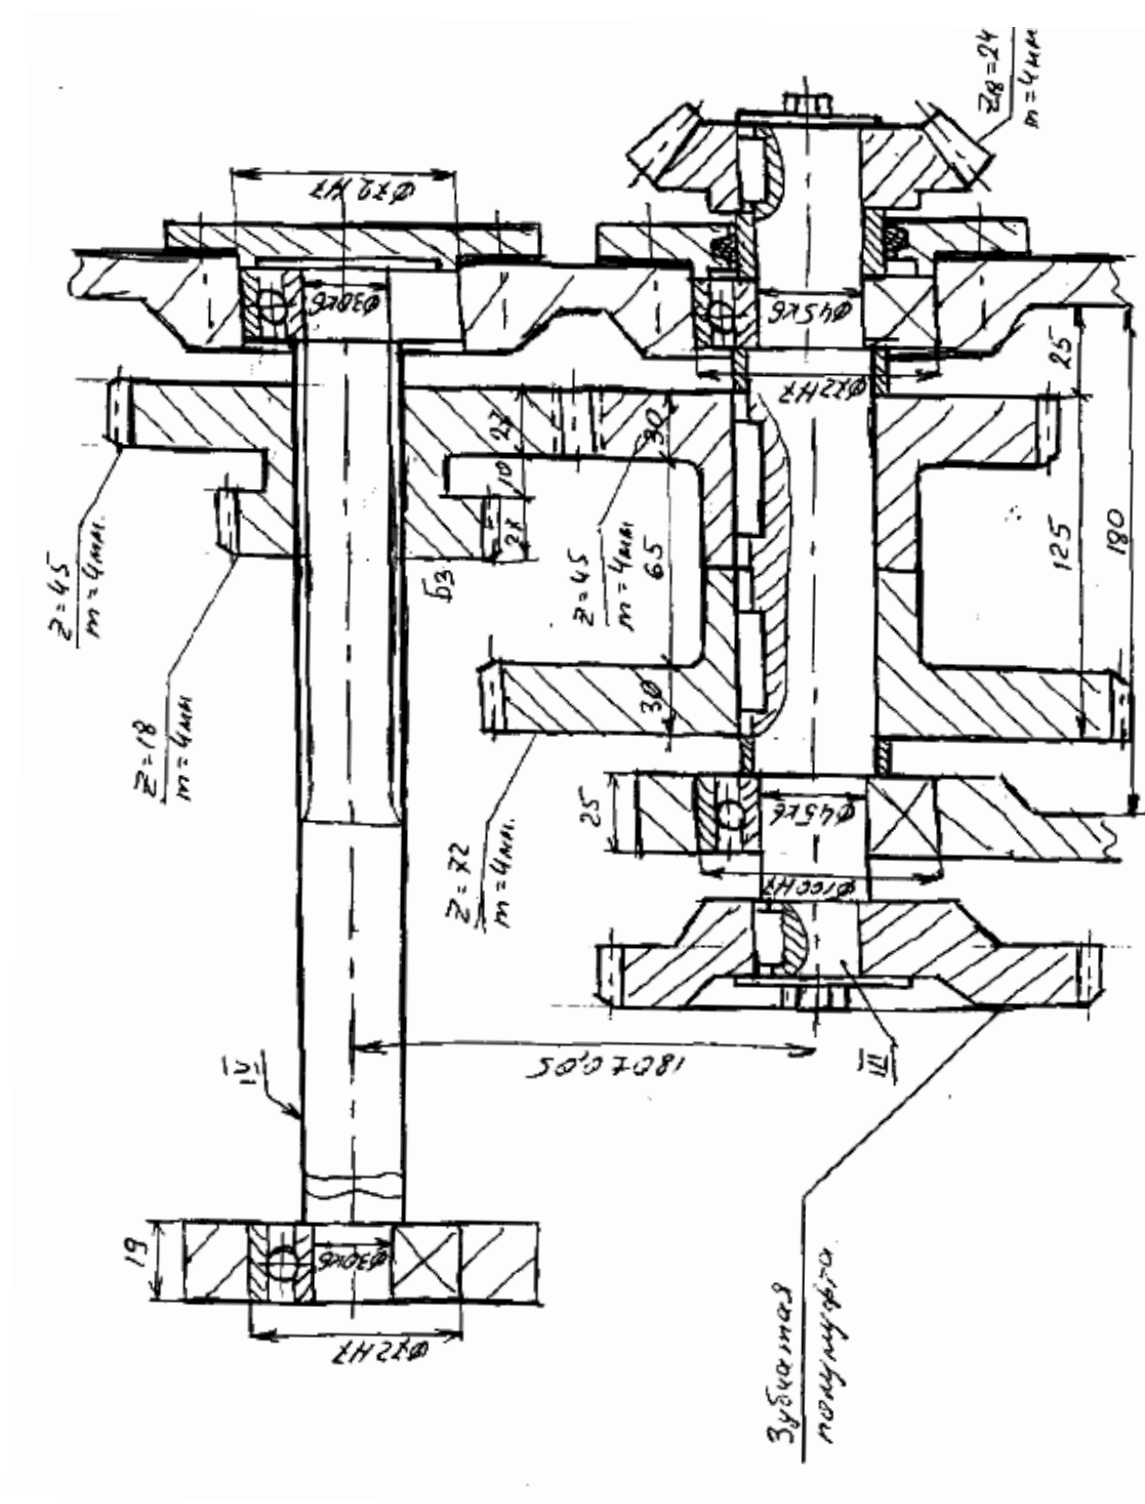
сборочный чертеж развертки наиболее нагруженной группы передач
